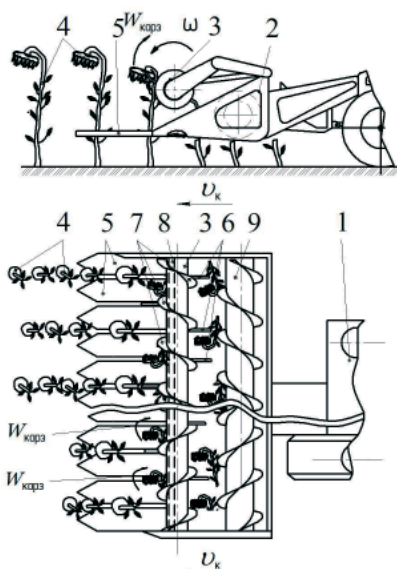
Технологическая схема работы шнека-мотовила: 1 – зерноуборочный комбайн; 2 – жатка; 3 – шнек-мотовило; 4 – стеблестой подсолнечника; 5 – стеблеподъемники; 6 – отсекатели; 8 – режущий аппарат; 9 – шнек-жатки; $W_{корз}$ – ускорение движения корзины; v_k – линейная скорость движения комбайна
